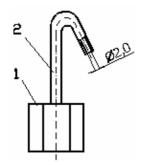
Контрольное приспособление 1- гайка накидная; 2-трубка
